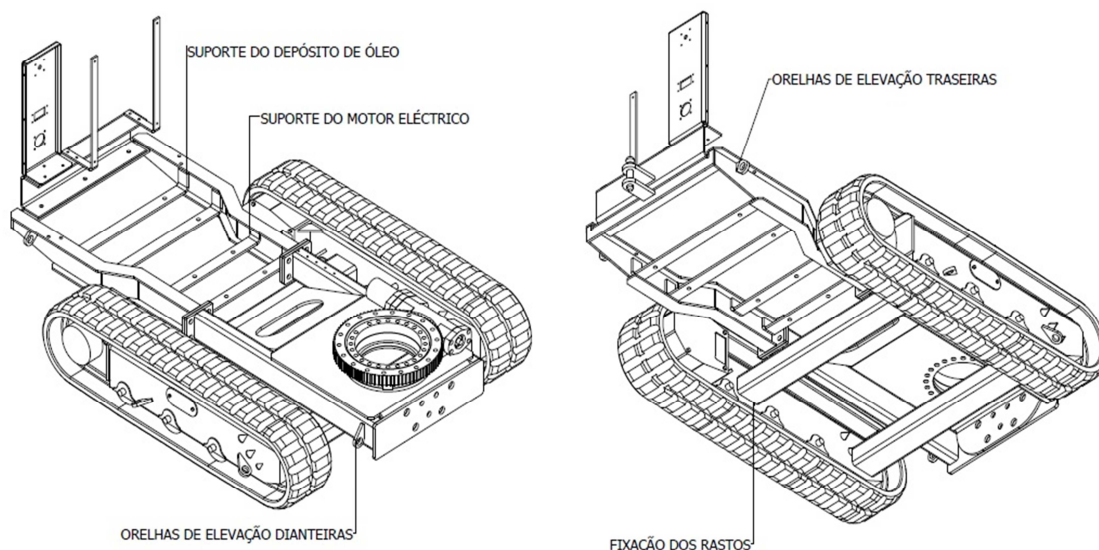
Localização das principais soldaduras dimensionadas
